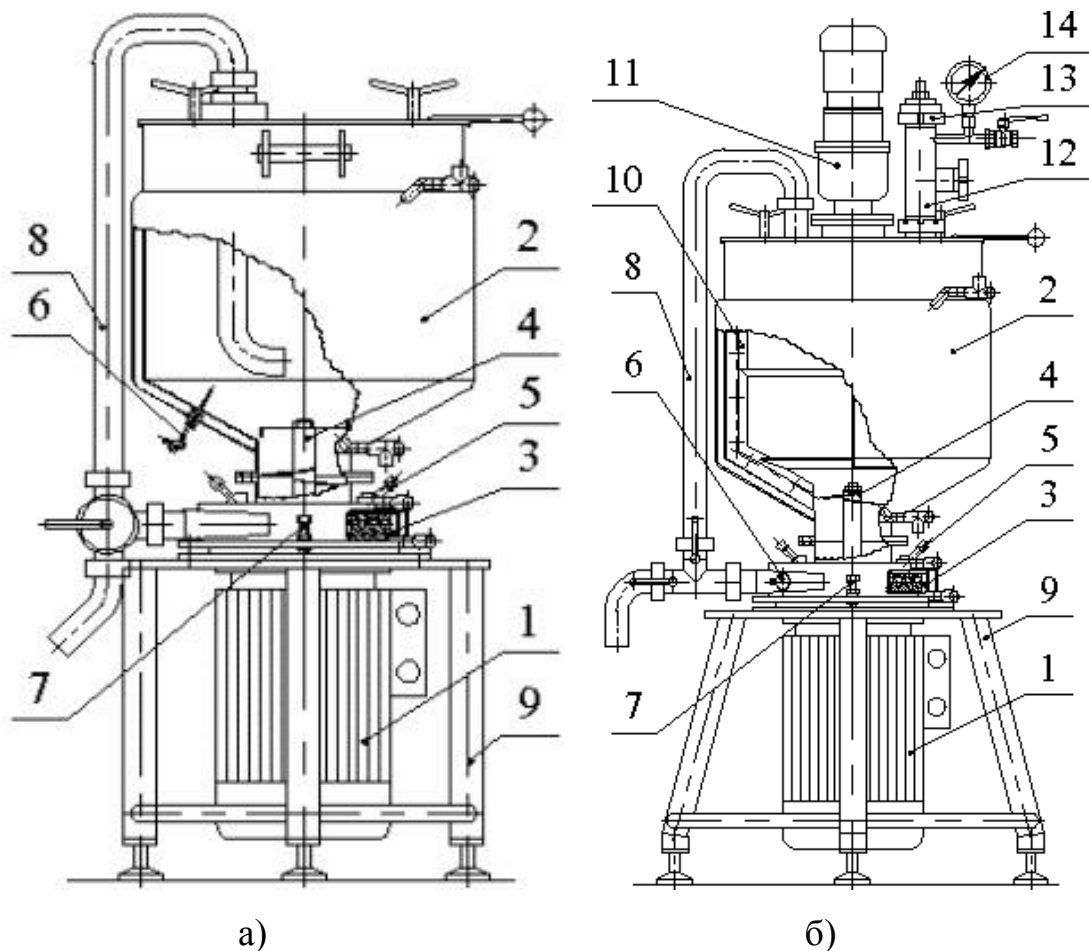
Гідродинамічна установка роторного типу розробки ВНИМИ
